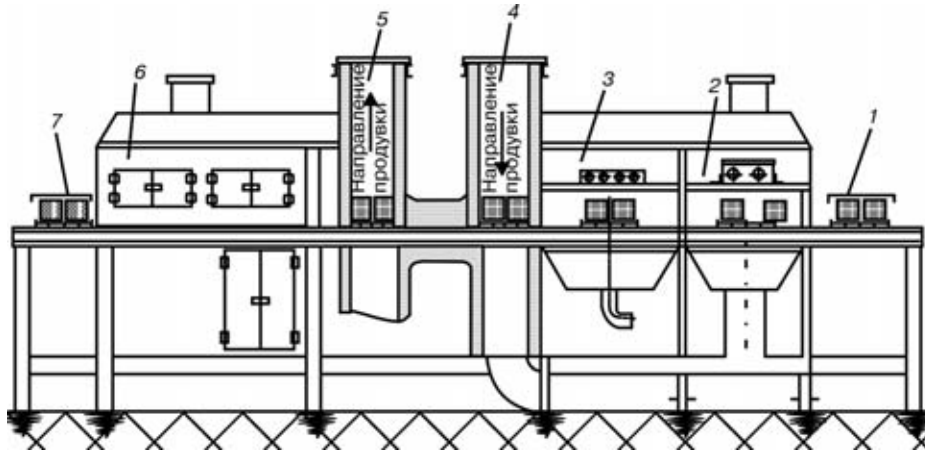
Схема печи спекания трубных пакетов (существующая): 1 — позиция загрузки; 2 — камера флюсования; 3 — камера продувки; 4 — камера предварительного подогрева; 5 — камера пайки; 6 — камера охлаждения; 7 — позиция разгрузки
